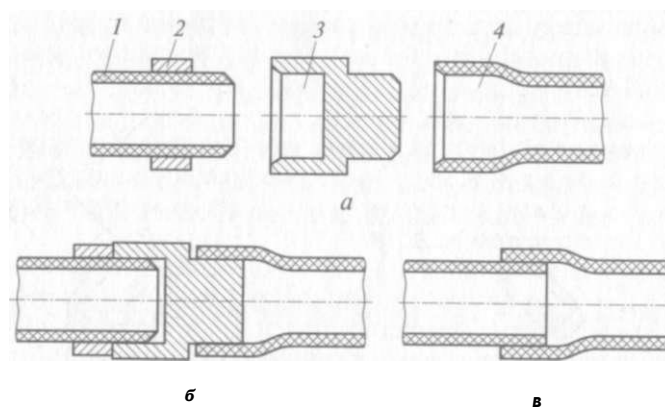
Схема сварки труб внахлест: а — центрирование и установка ограничительного хомута: / — прямой конец трубы; 2 — ограничительный хомут; 3 — нагревательный инструмент; 4 — конец трубы с раструбом; б — нагрев и оплавление свариваемых концов труб; в — соединение свариваемых труб
